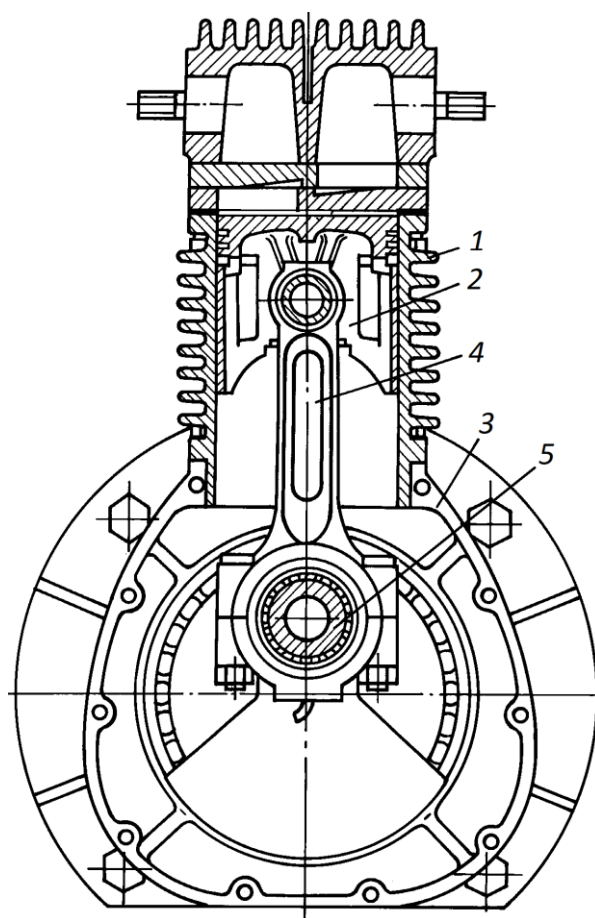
Циліндро-поршнева група пневматичного компресора
